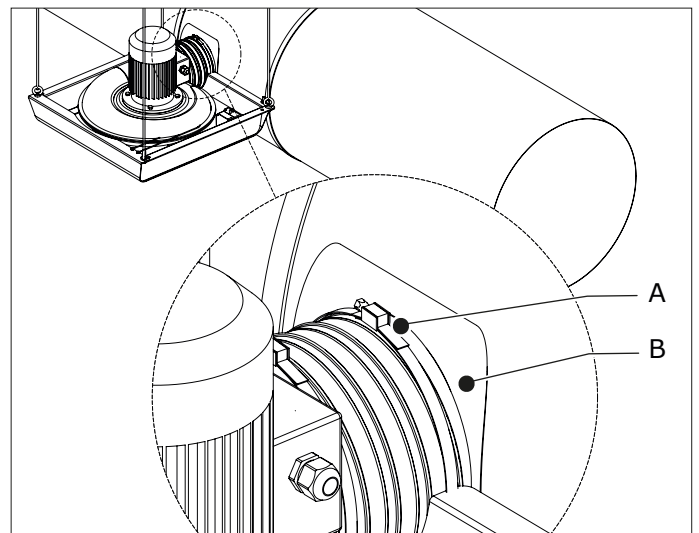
Montaje de la manguera en la pieza de injerto
